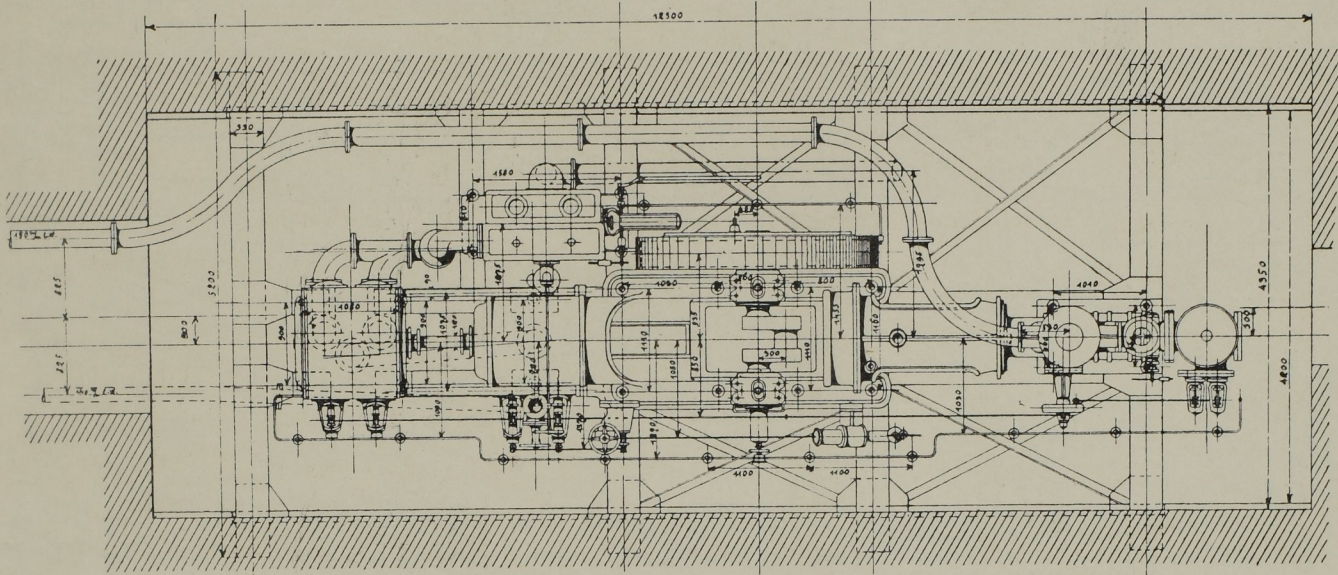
Grundriss der Maschine. Masst. 1:75.
